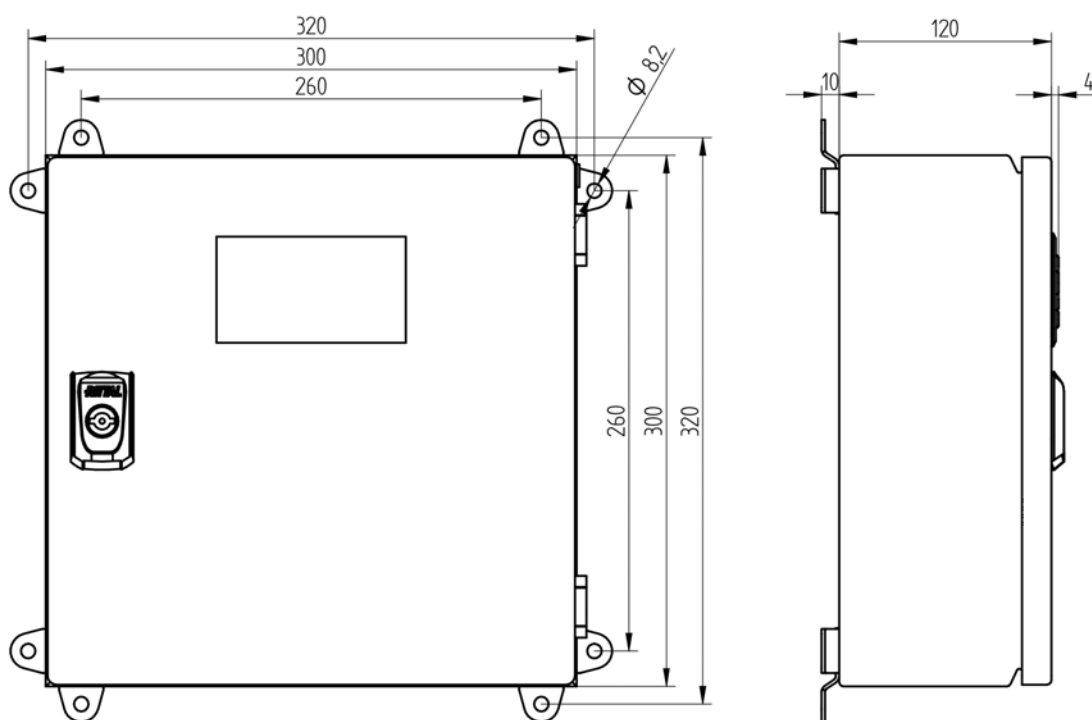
Plan coté LT3-F dans boîtier avec supports muraux vertical/horizontal et UI300-LT-V2 (dimensions en mm)
